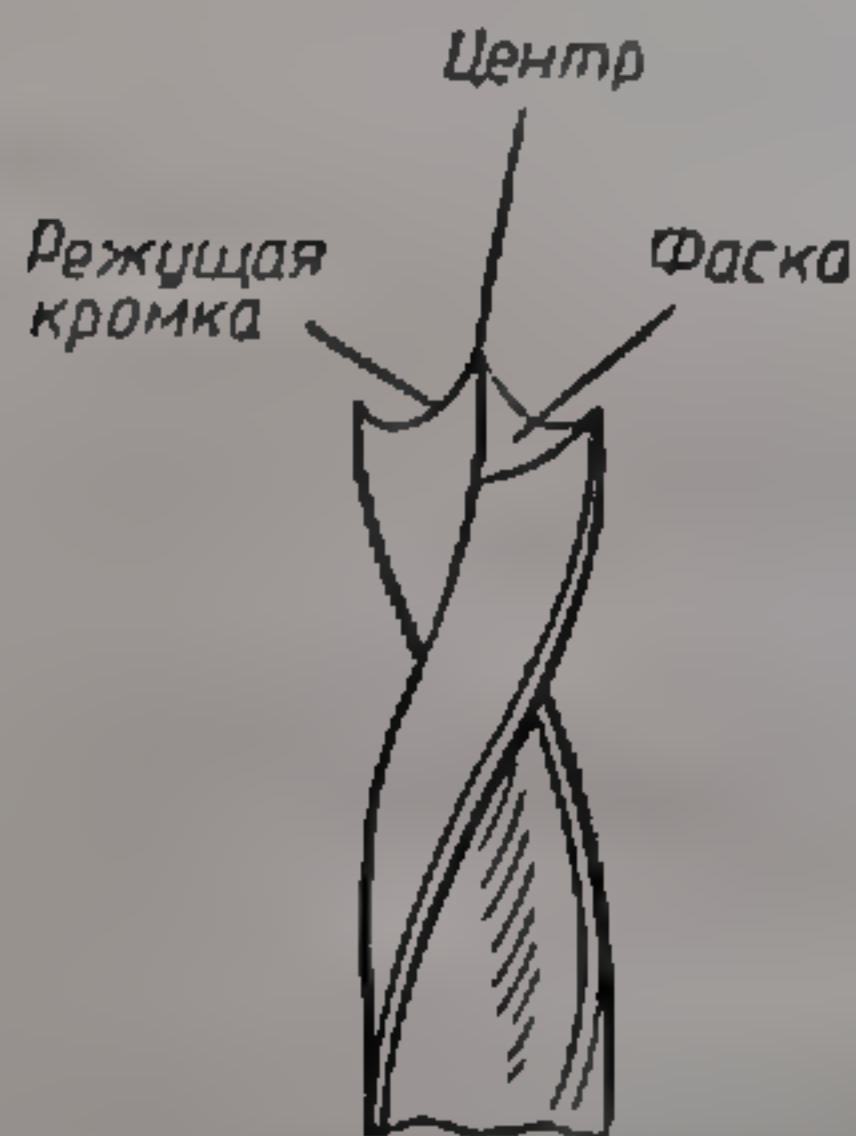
Сверло для сверления отверстий для круглых шипов.
